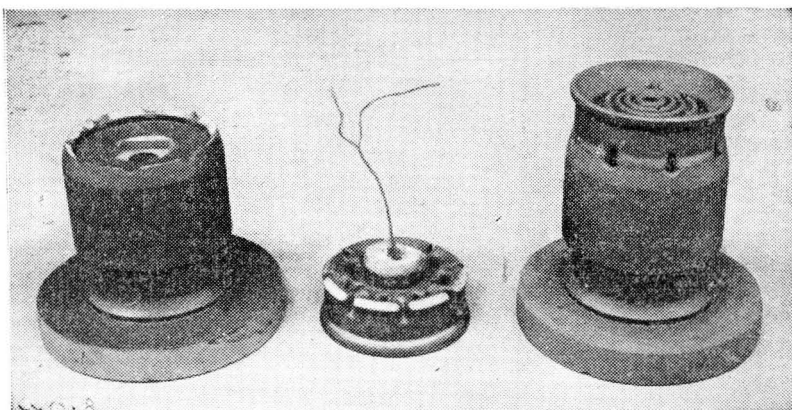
Machos para emprêgo em moldagem de pistões de locomotiva Diesel-elétrica.
